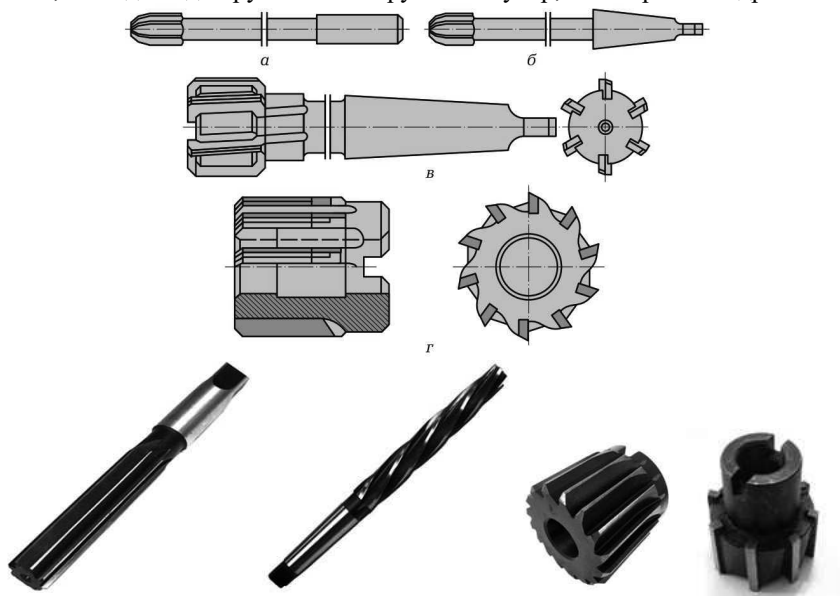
Розгортки: а, б – цілісні; в – насадна; г – насадна, оснащена пластинами із твердого сплаву
